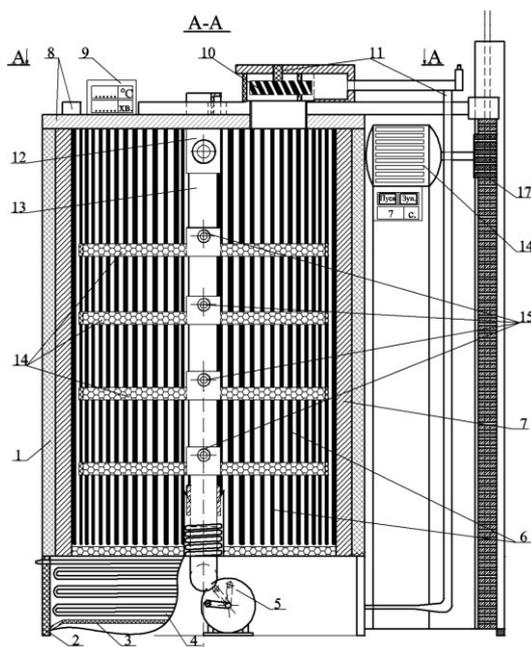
Промысленно-исследовательский образец вертикальной цилиндрической ИК-сушки ВЦ-ИК-20: 1 – вертикальная цилиндрическая рабочая камера; 2 – стойки; 3 – распределительная решетка для поступления свежего воздуха; 4 – трубчатый теплообменник; 5 – ФВМ; 6 – продольные рабочей камере ИК-излучатели; 7 – отражающая фольга с теплоизолирующим листовым алюфомом; 8 – крышка с затяжными фиксаторами; 9 – блок САУ; 10 – вентилятор, установленный в вытяжной улитке; 11 – нагнетающий канал; 12 – фиксатор; 13 – штатив; 14 – сетчатые лотки; 15 – подъемный механизм; 16 – монтажные шпильки; 17 – прямозубая направляющая
